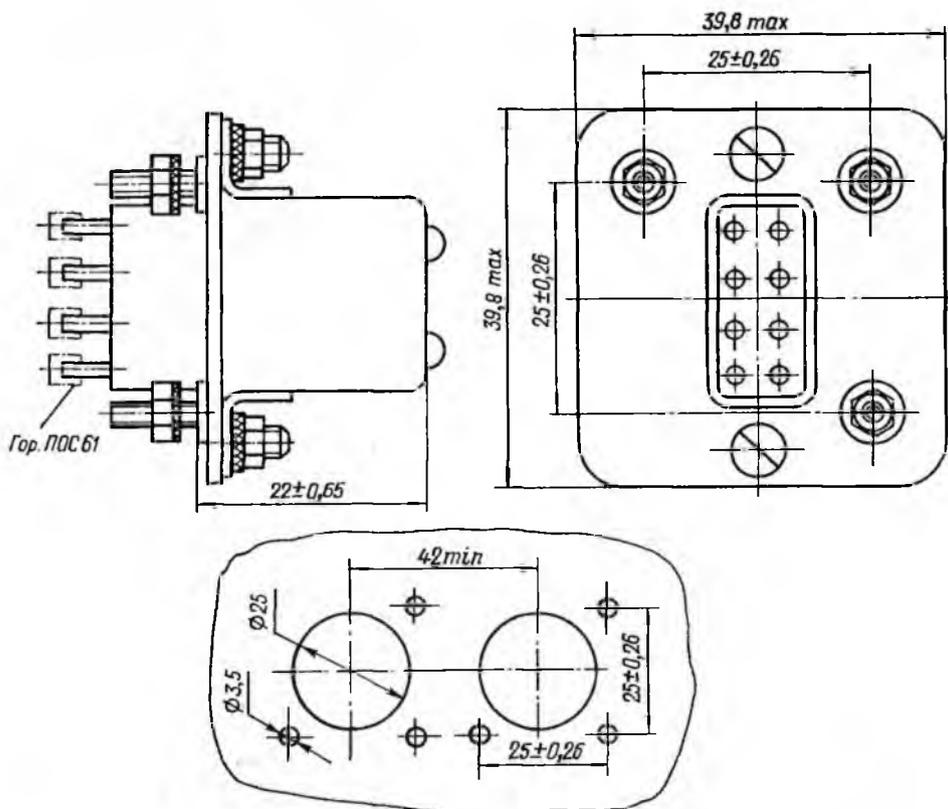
Конструктивные данные реле РЭС59В (с платой для болтового крепления) и разметка для крепления
